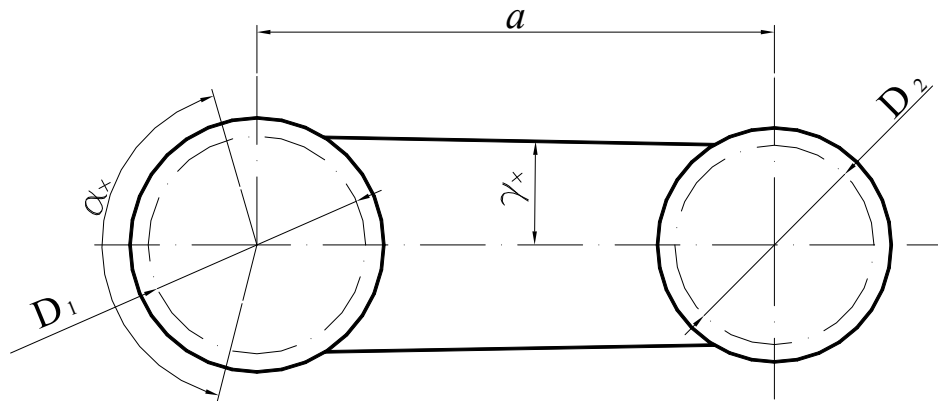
Розрахункова схема клинопасової передачі приводу
